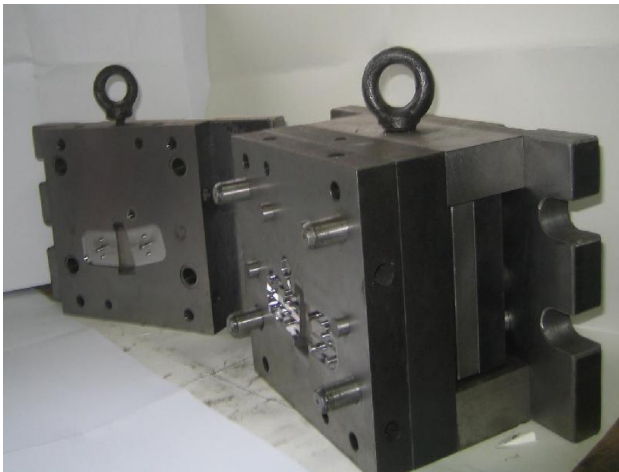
Готова пресформа для виготовлення пресованих деталей.
